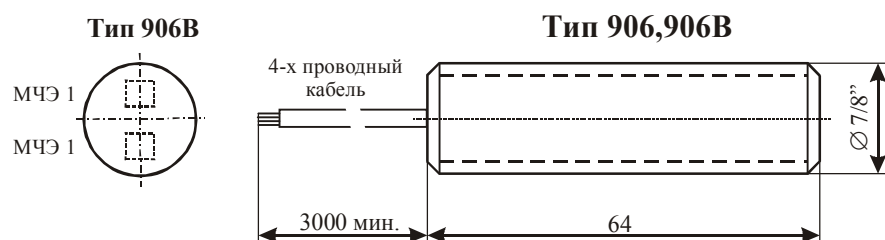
Внешний вид и габаритные размеры датчиков типа 906
